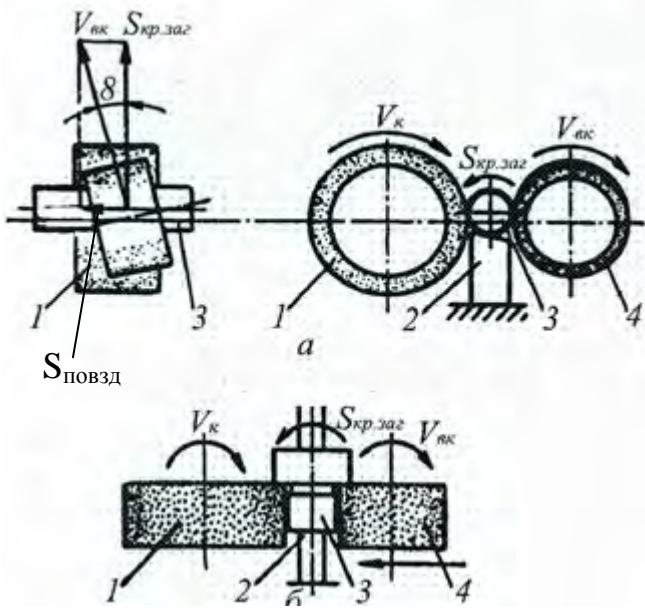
Схеми оброблення заготовок на безцентрово-шліфувальних верстатах
